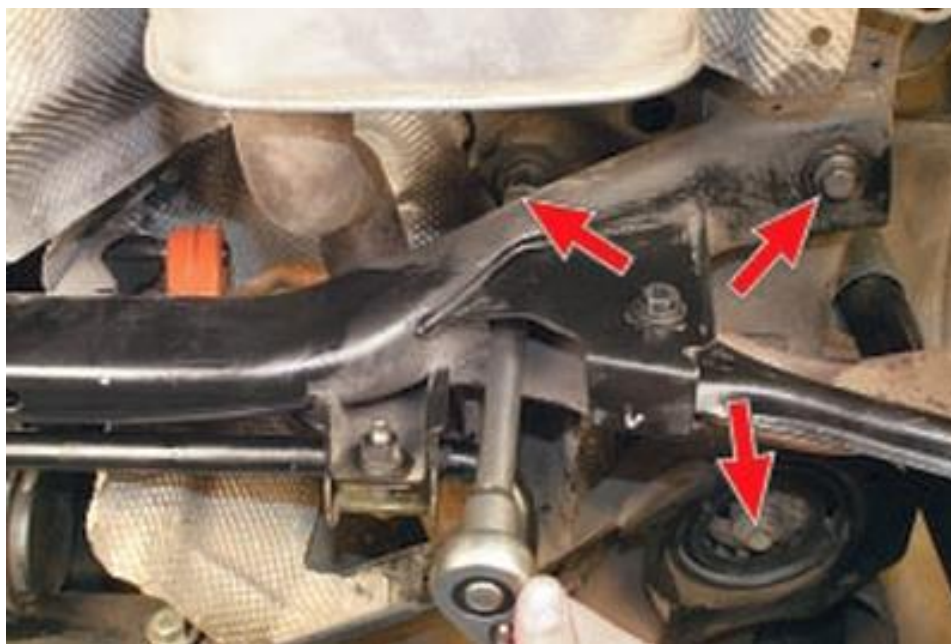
Відкручування болтів кріплення поперечки до кузова
